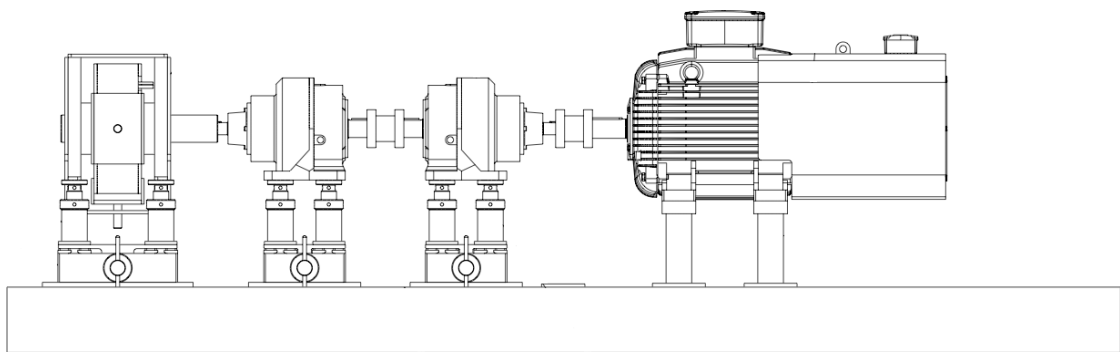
Bancada - Motor, Redutor, Caixa Multiplicadora e Gerador
